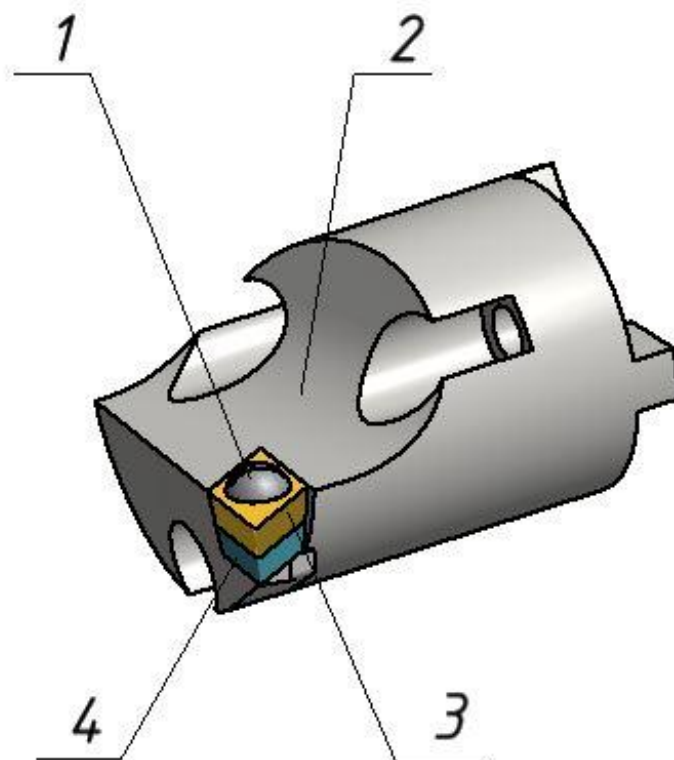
Оправка . 1) кріпильний гвинт; 2) тіло різця; 3) ріжуча пластина;
